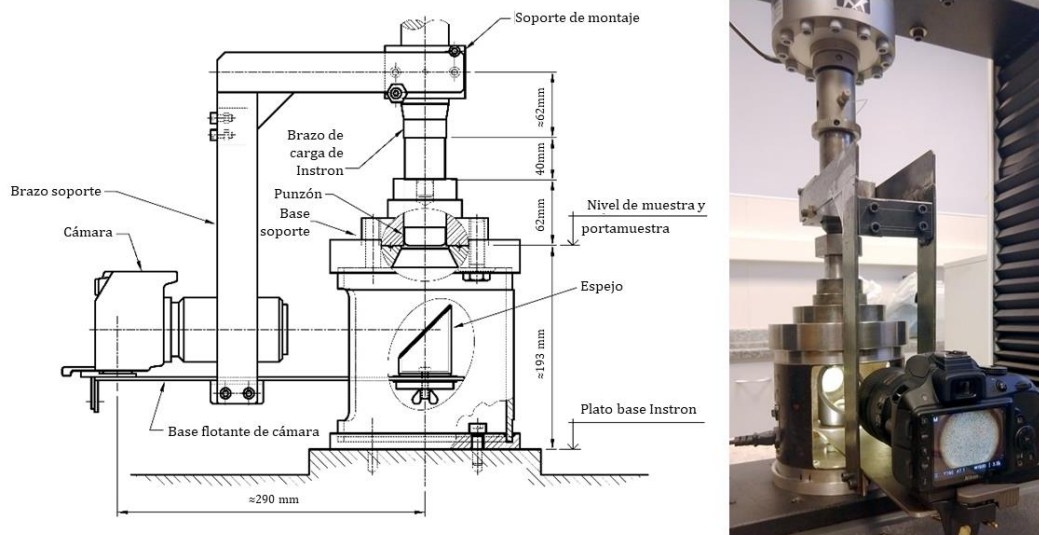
Dispositivo miniatura de ensayos de conformado Marciniak montado en máquina de ensayos universales.
